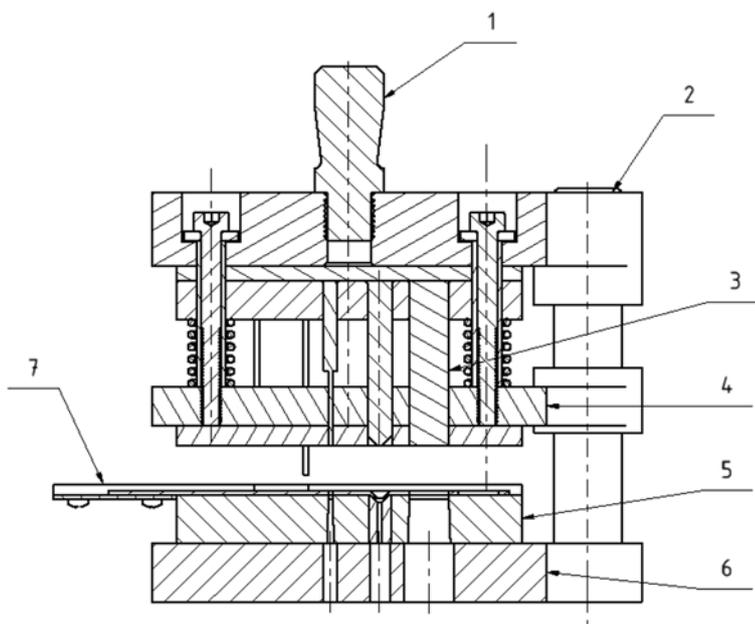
Ausstanz-Biegewerkzeug für Schnellspanner
